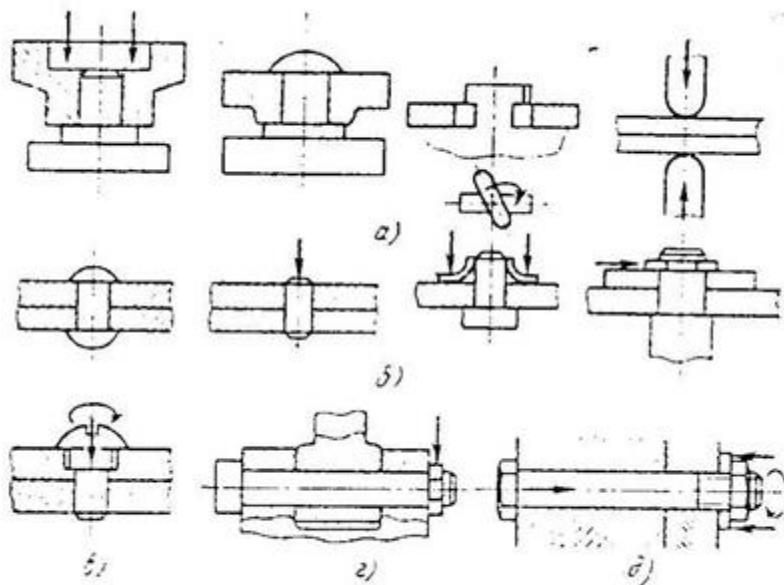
Виды креплений по сложности выполнения автоматической сборки
